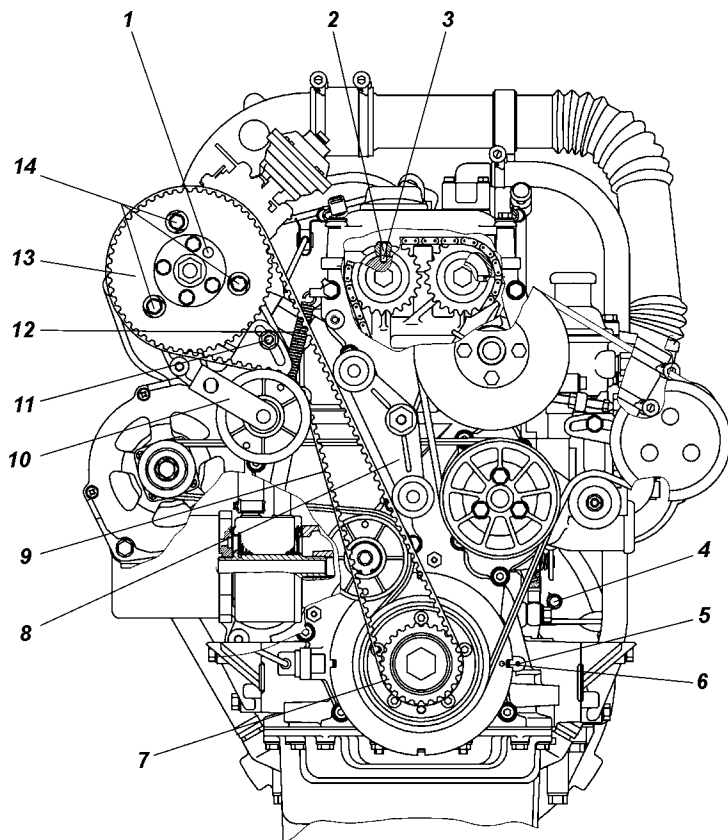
Расположение меток и отверстий под штифты для замены ремня привода ТНВД:
